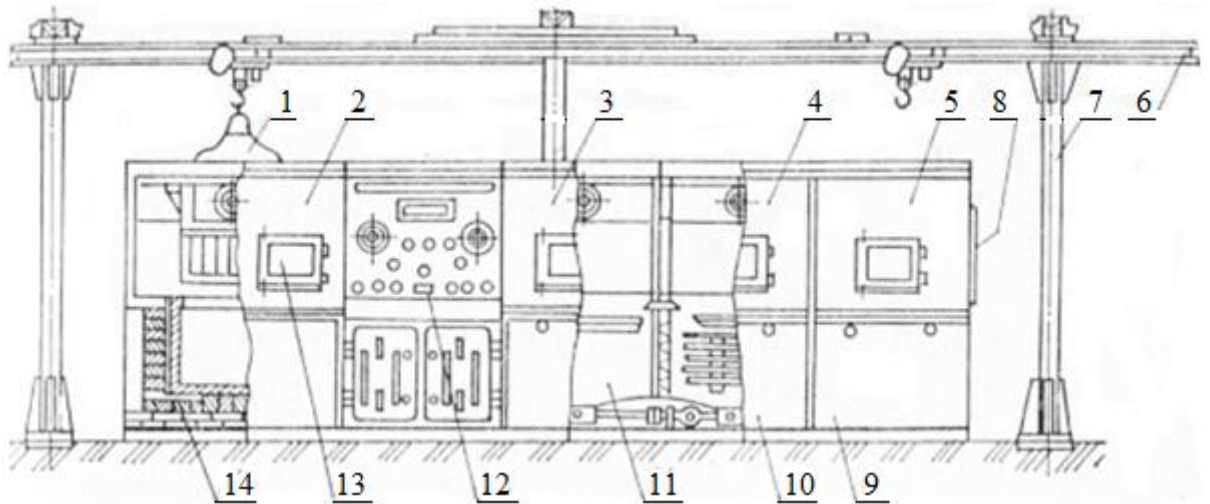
Установка для очистки деталей в расплавах солей:
